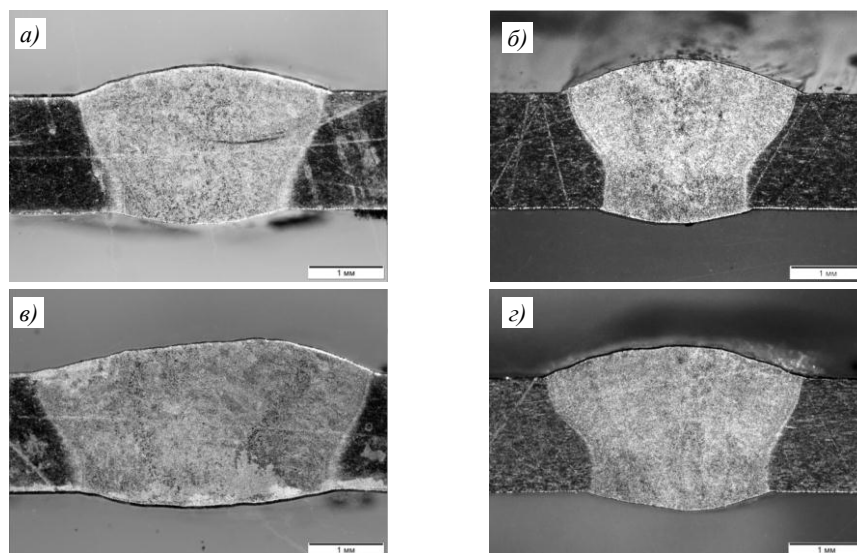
Макроструктура ($\times 25$) сварных соединений образцов, выполненных одним (а, б) и двумя (в, з) проходами лазерной сварки на скоростях 0,03 (а, в) и 0,05 м/с (б, з)
